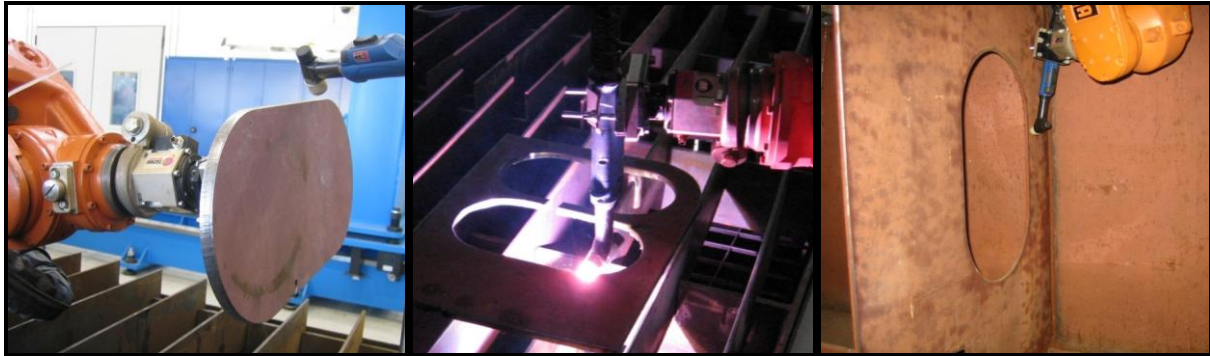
3 mögliche Konzepte für das Plasmaschweißverfahren
